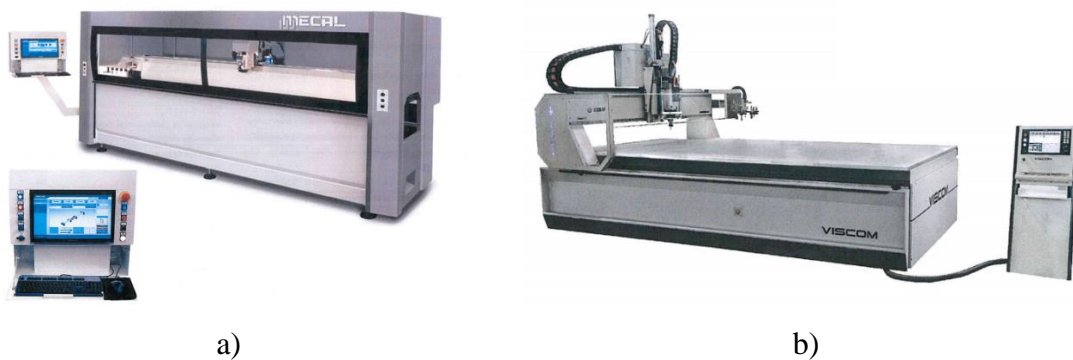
Equipamentos de maquinação: a) centro de maquinação; b) CNC de chapa.
